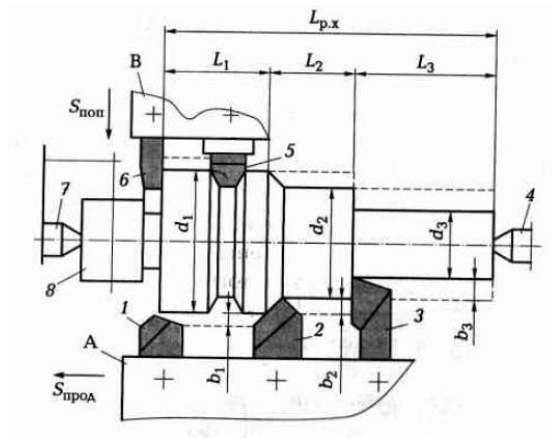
Схема обробки на багаторізцевому верстаті
